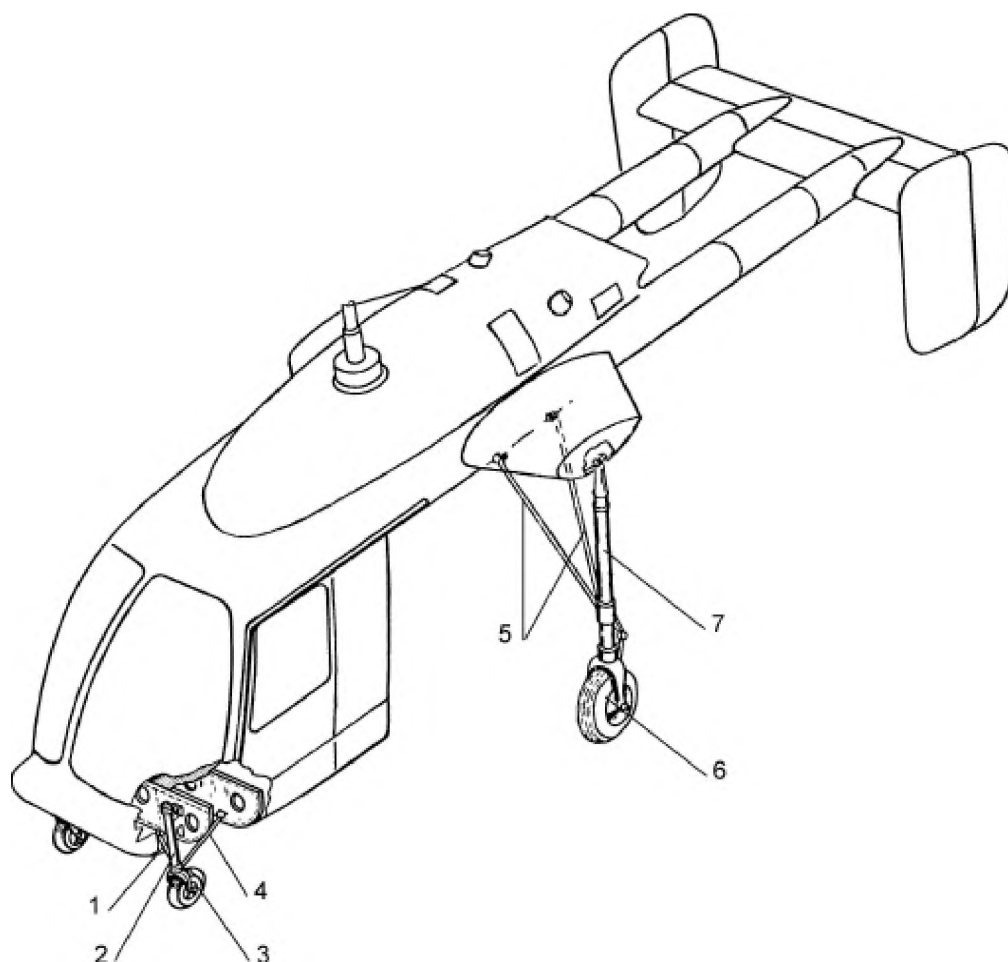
Компоновка колесного неубирающегося шасси вертолета Ка-226А [16]:
